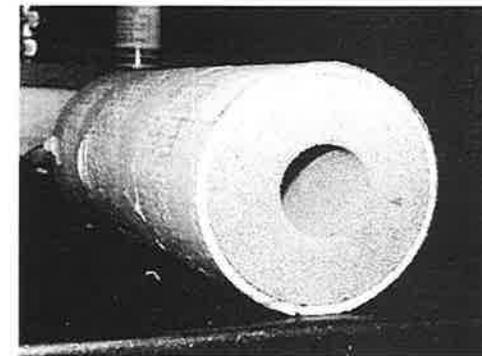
Test-Schalldämpfer aus einer metallischen Hohlkugelstruktur, Außendurchmesser: 150mm, Innendurchmesser: 50mm, Länge:350mm, Material 316L
